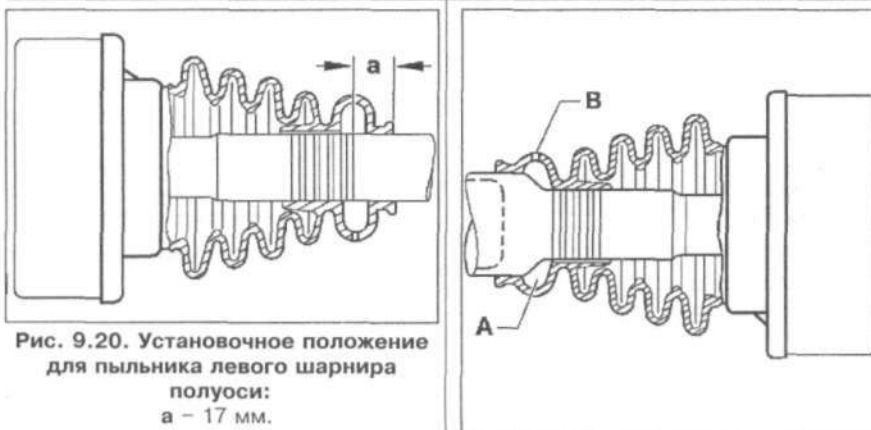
Установочное положение для пыльника левого шарнира полуоси:
